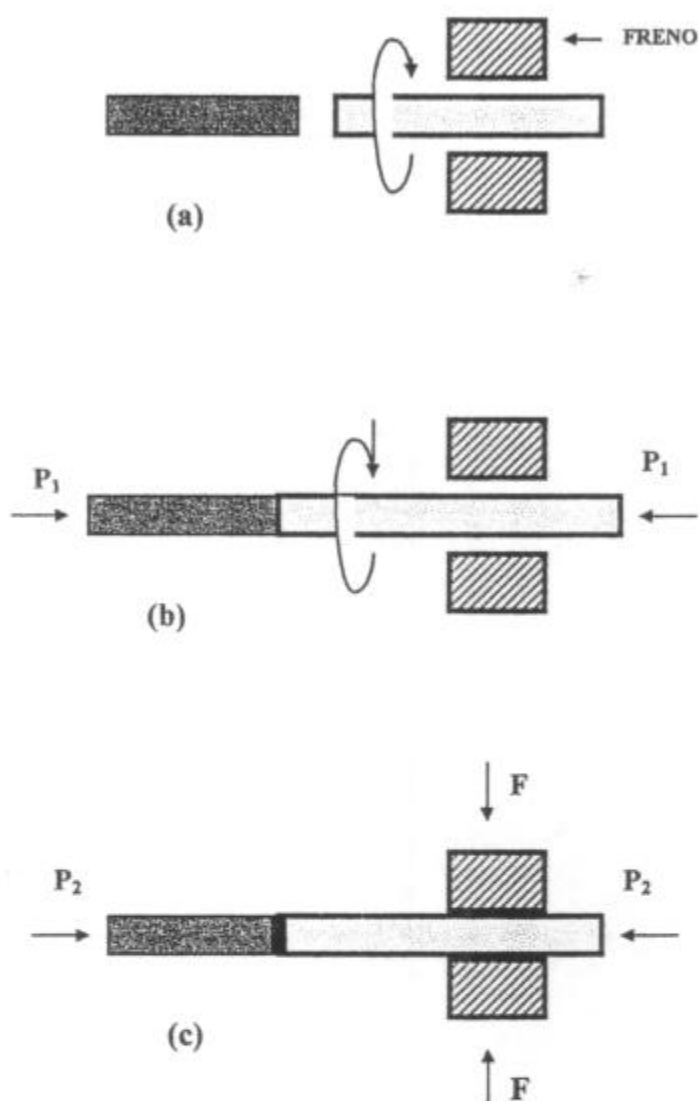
Operaciones básicas de la soldadura por fricción convencional.
